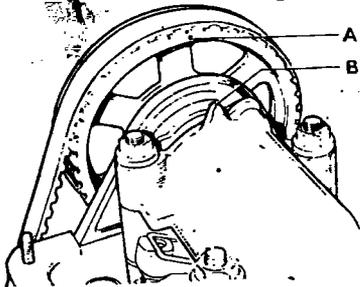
Проверка совпадения установочной метки на шкиве распределительного вала с меткой на корпусе подшипников: А - метка на шкиве; В - метка на корпусе подшипников
